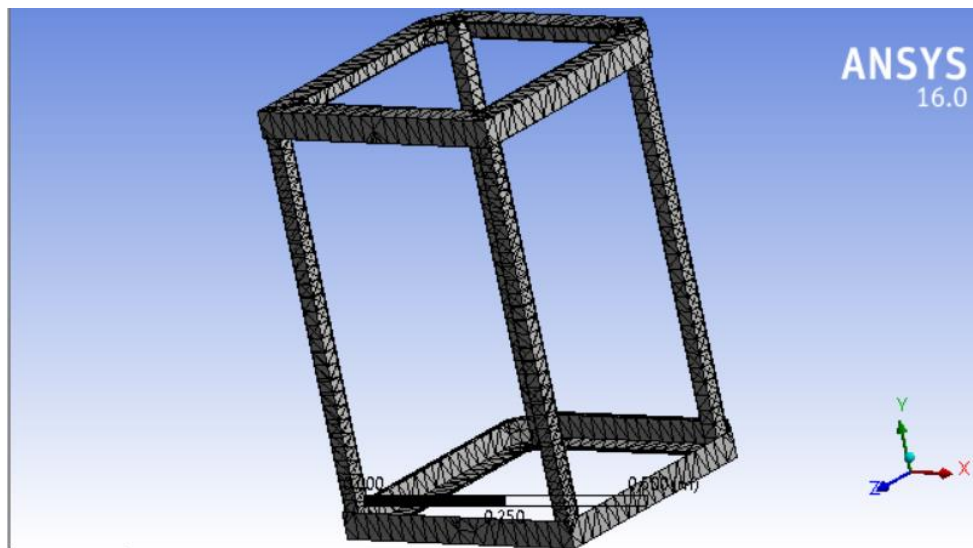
6 Aplicación de mallado a la estructura de soporte [Autor]
